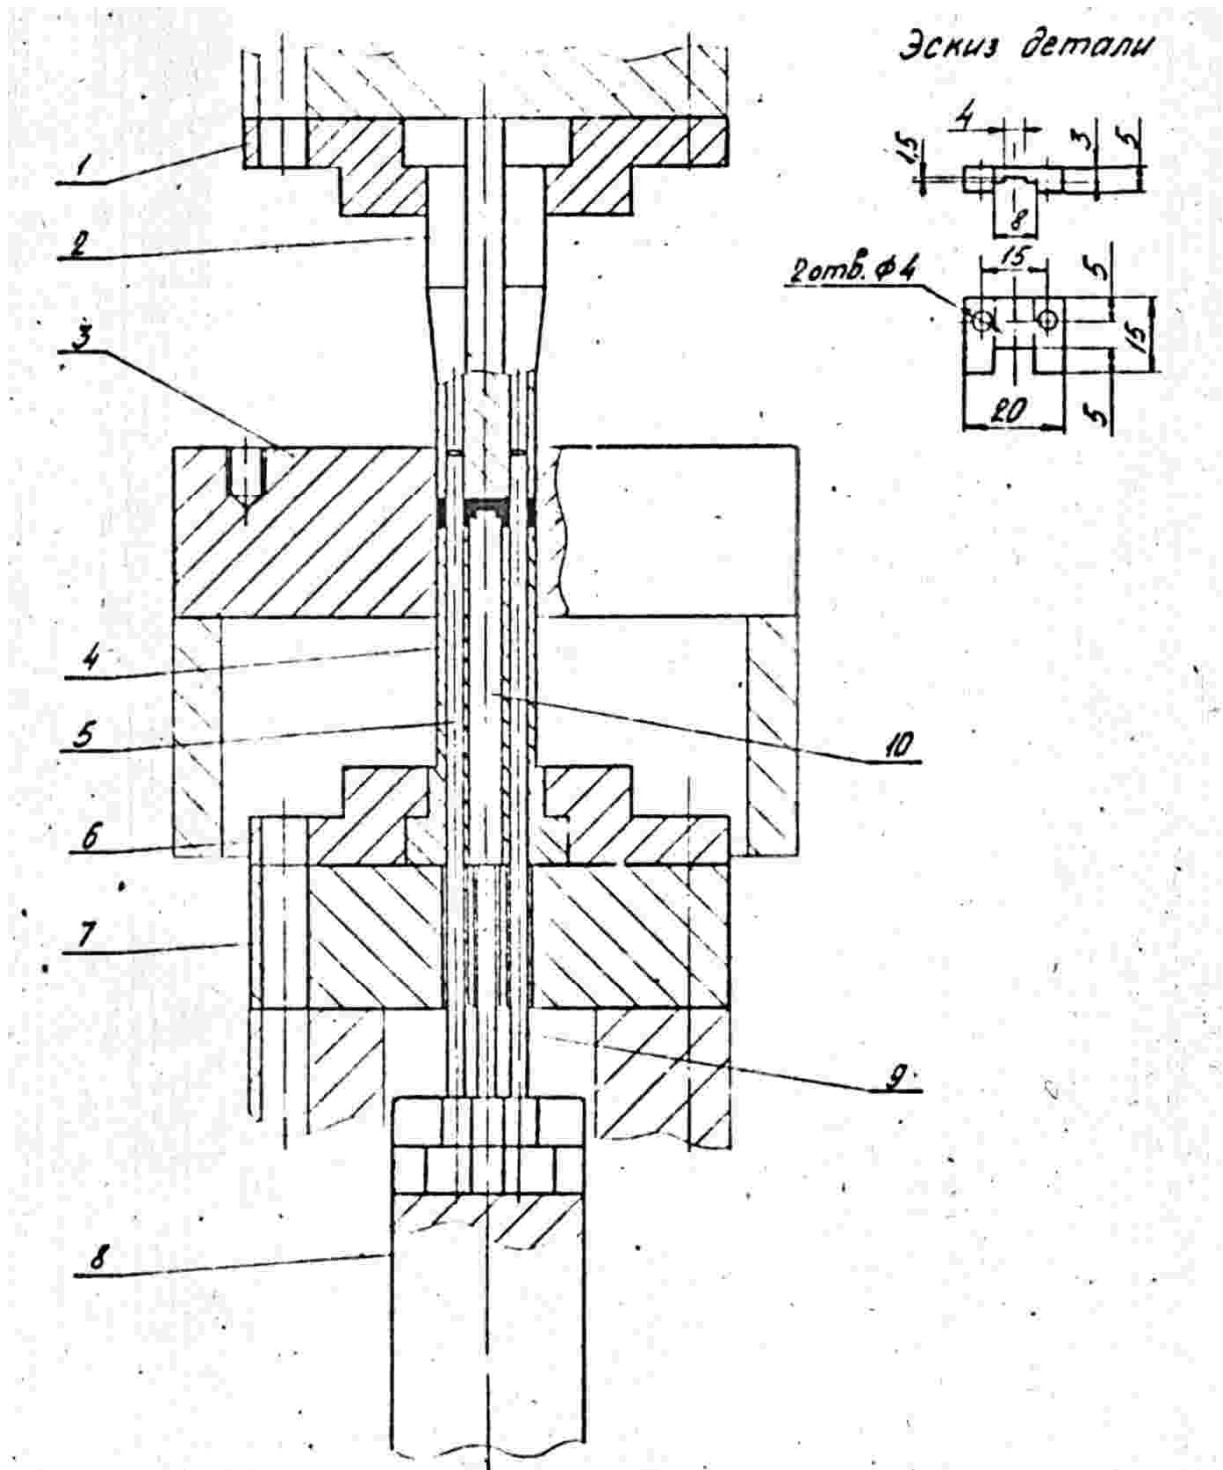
Конструкция рабочих частей пресс-форм (матрица, пуансон, стержень) для прессования изделия сложной формы и несколькими переходами по высоте
